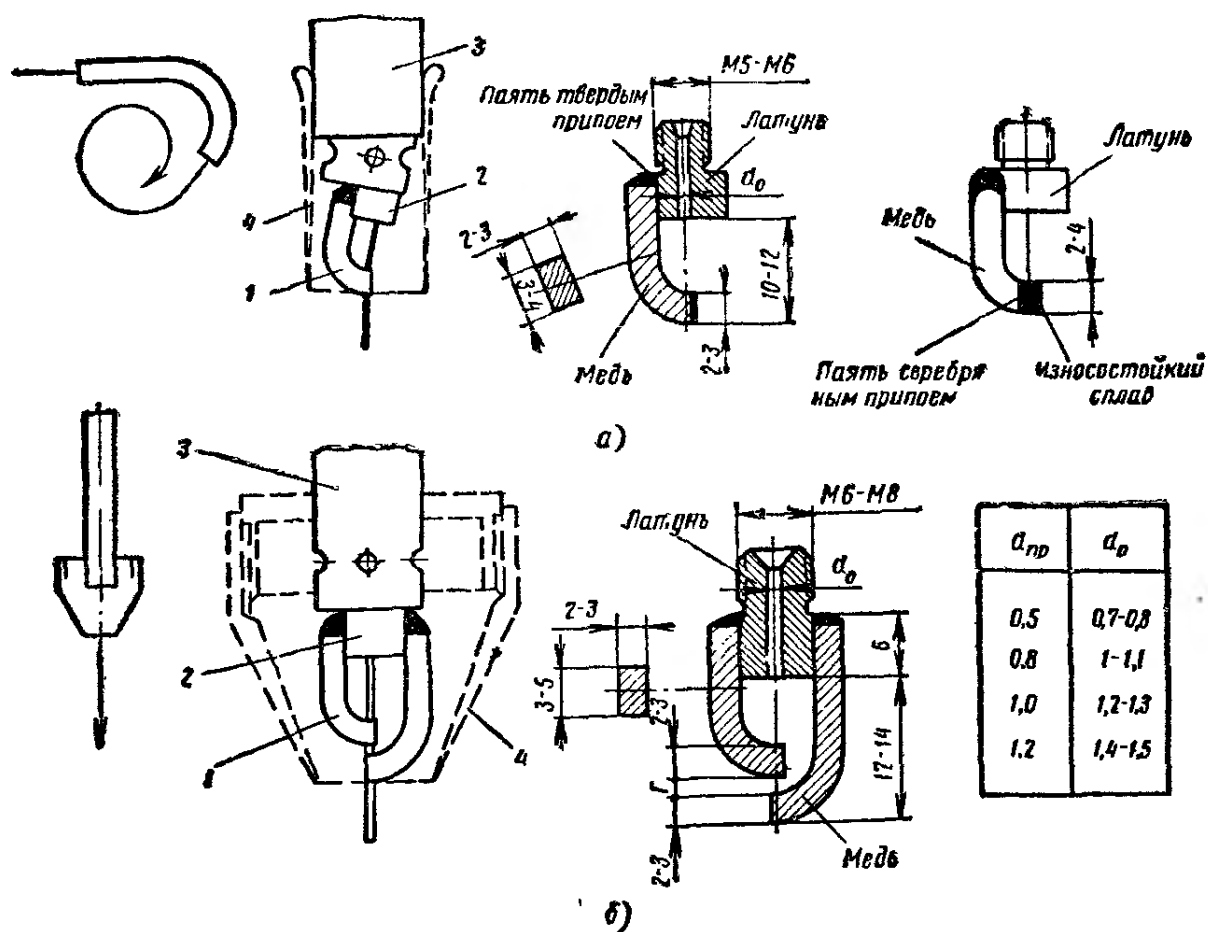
Типы контактов держателя для изогнутых (а) и прямых (б) мундштуков, для сварки проволокой 0,5—1,2 мм:
